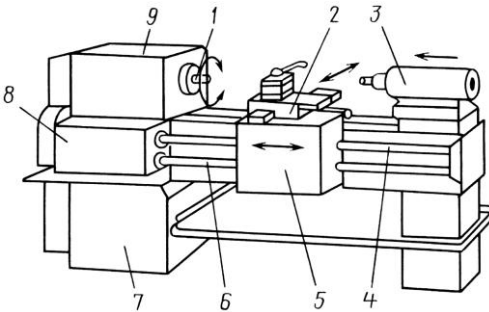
Компонування токарно-гвинторізного верстата
